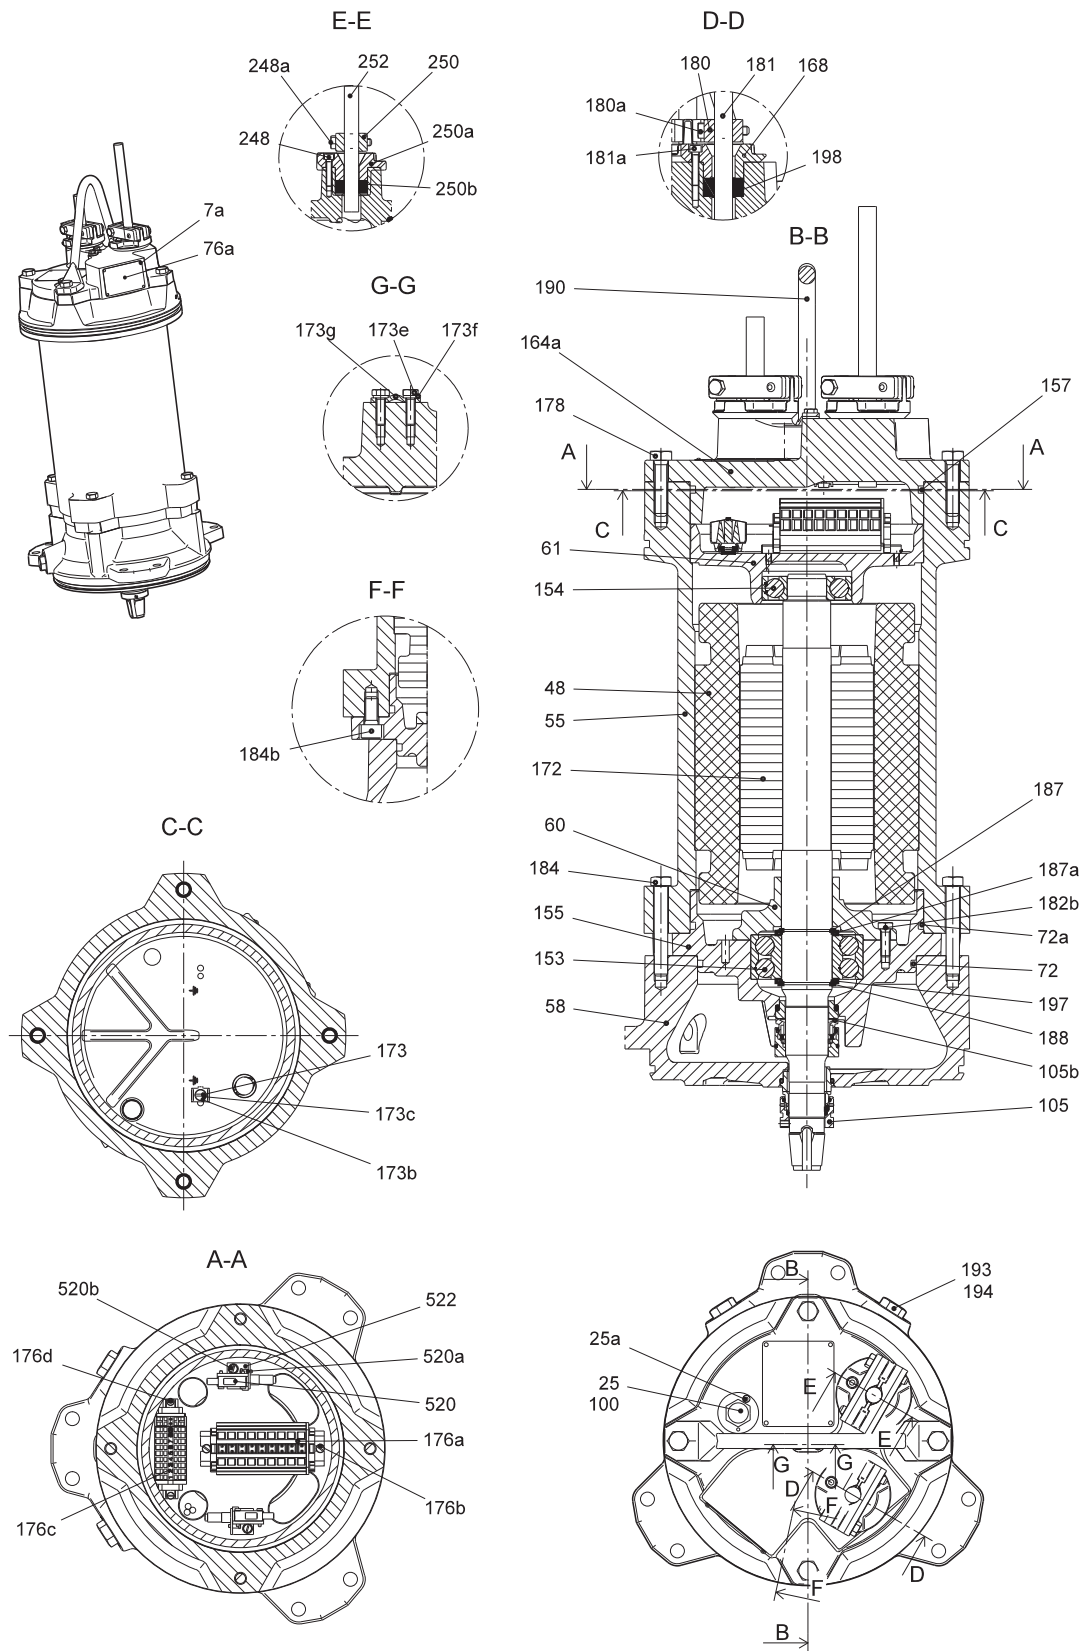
Взрывозащищённый двигатель, без охлаждающего кожуха
